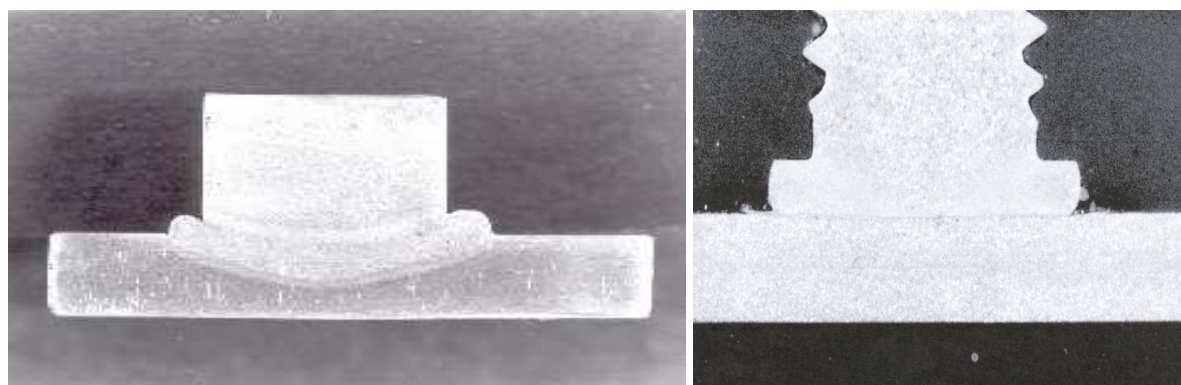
Princip metody přivařování s hrotovým zážehem
